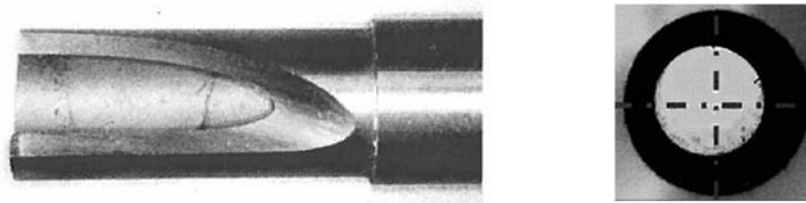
Kernbohrwerkzeug mit exzentrischem Kern Seitenansicht (links) und Querschnitt (rechts) nach *Hagino et al.* (2013)
